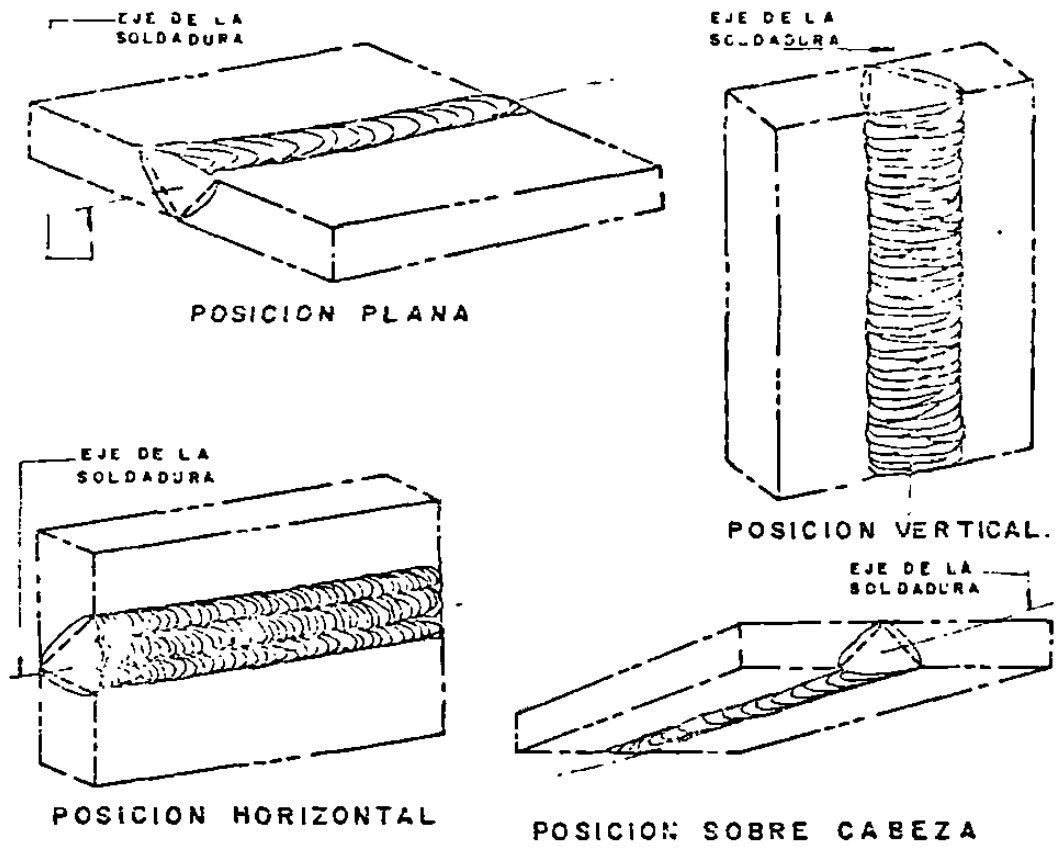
POSICION AL SOLDAR PARA SOLDADURA DE RANURA
